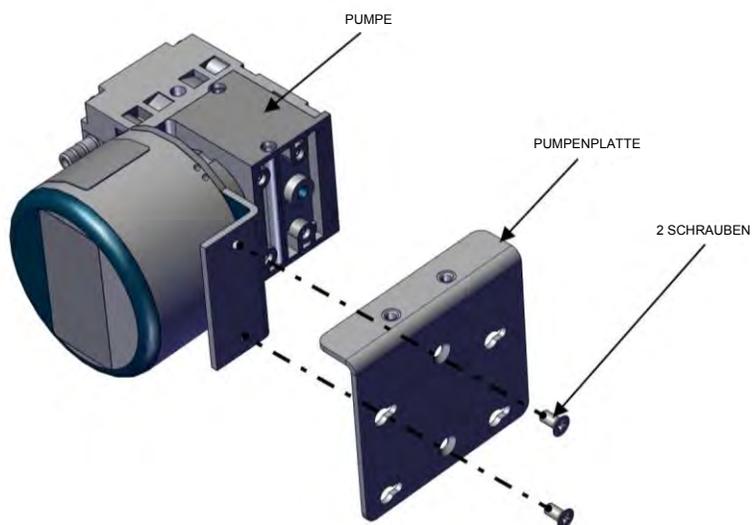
Austausch der Pumpe, Schrauben lösen
